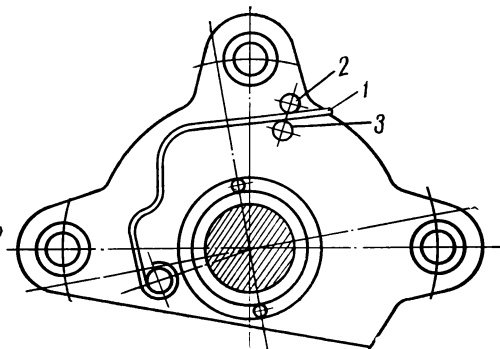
Общий вид фиксатора каретки прижимного ролика
